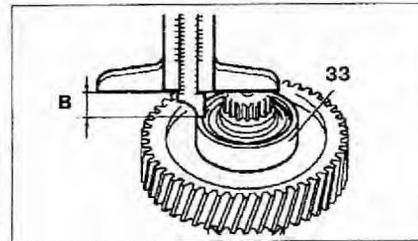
Измерение расстояния В от конца промежуточного вала до внешнего кольца подшипника 33, используя штангенциркуль.
